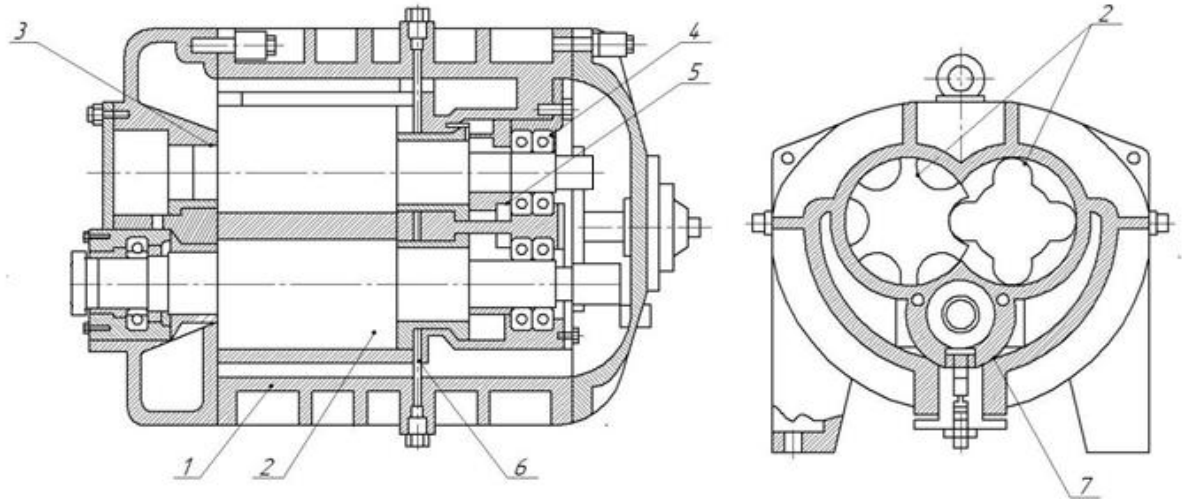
Общий вид винтовой компрессорной установки
